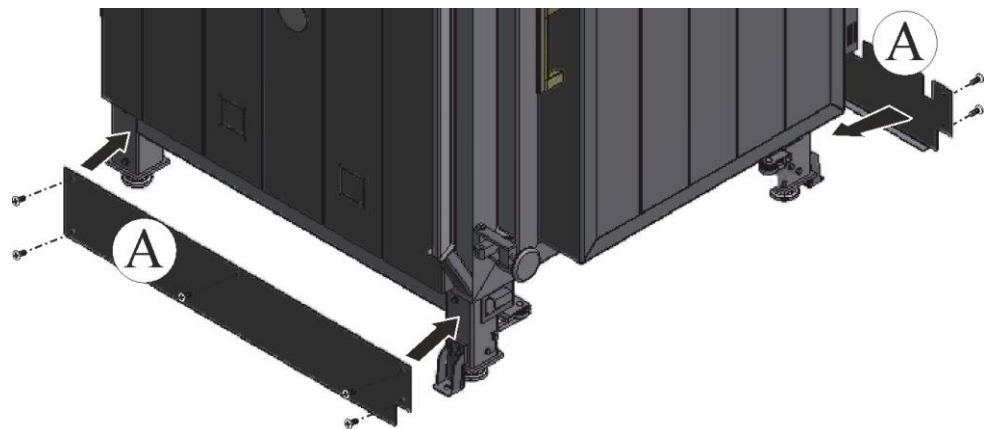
Montagem das chapas laterais (semelhante à figura)
